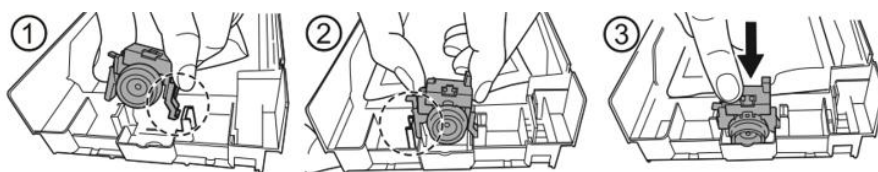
Встановлення чорнильного резервуару в корпус картриджа
